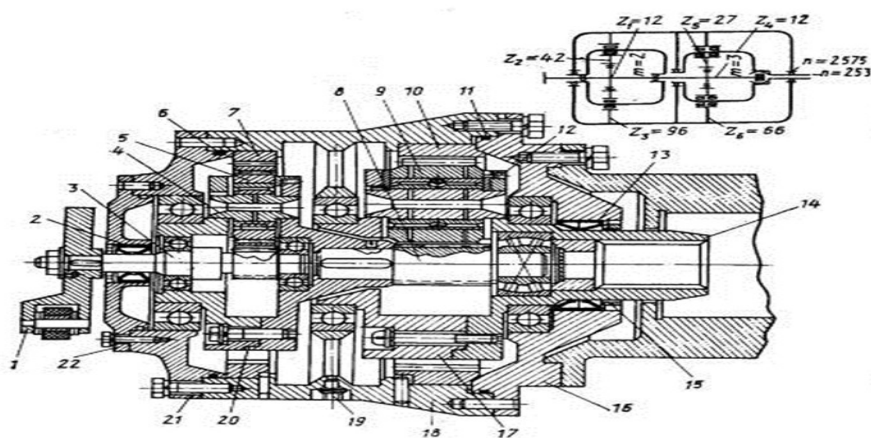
Планетарний редуктор центрифуги ФГШ-401К-01:
